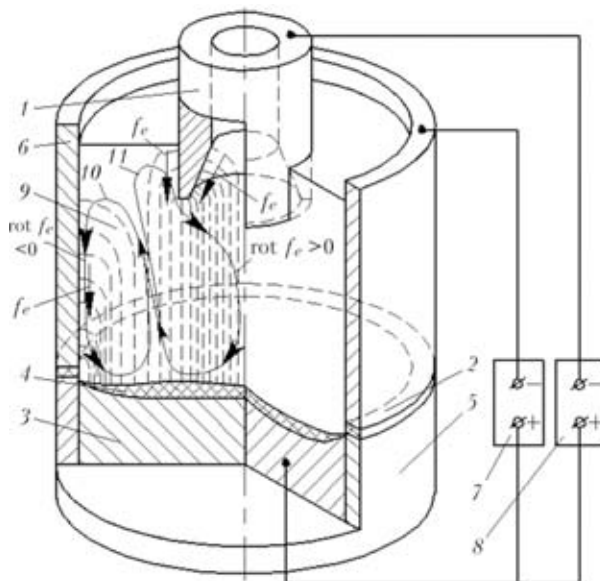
Схема распределения тока и движения шлака в исследуемой (рис. 1) модели СК: 1, 2 и 5-8 — см. обозначения рис. 1; 3 — наплавленный металл; 4, 9 — соответственно металлическая и шлаковая ванны; 10, 11 — потоки шлака; штриховыми линиями показаны линии тока
